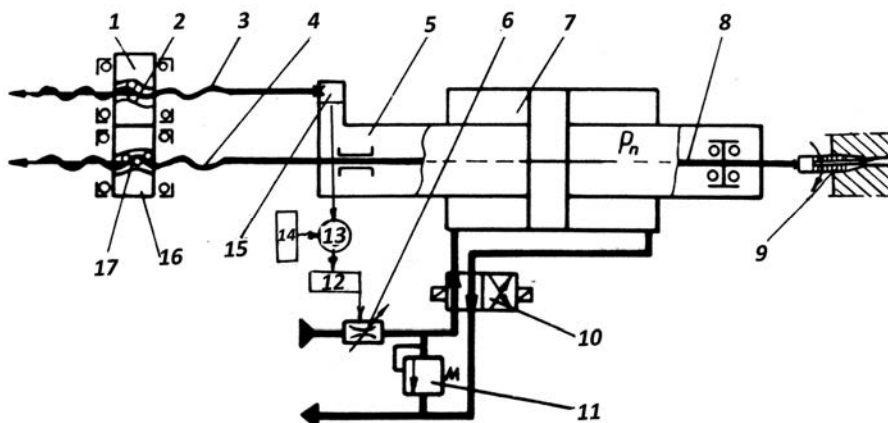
Схема передаточного механізму і перетворювача поступального руху в гвинтовий
